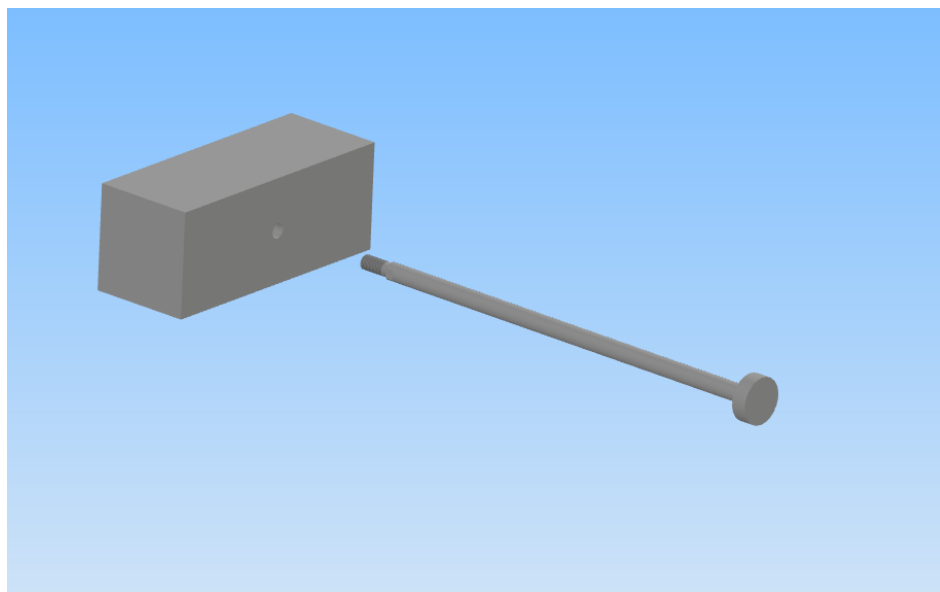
Vista explosionada del ensamble mostrado en la figura 3.60.
